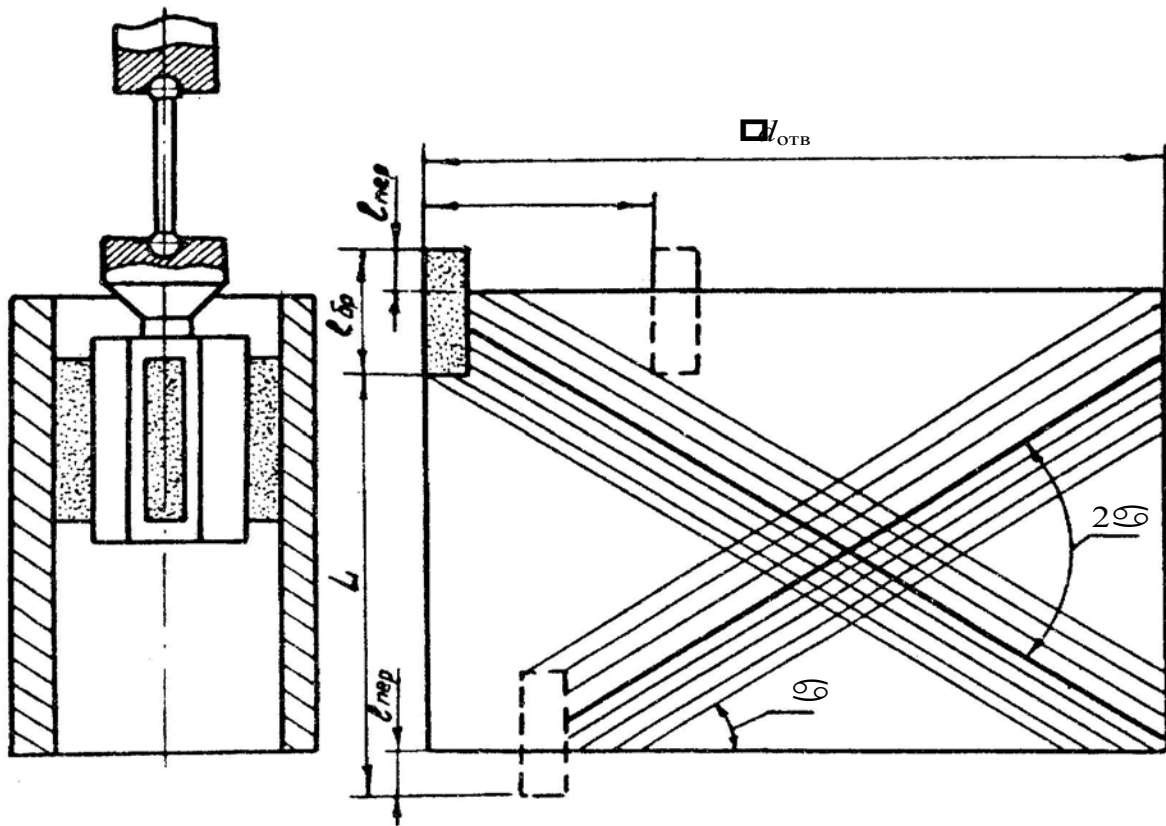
Схема обробки внутрішньої поверхні деталі
